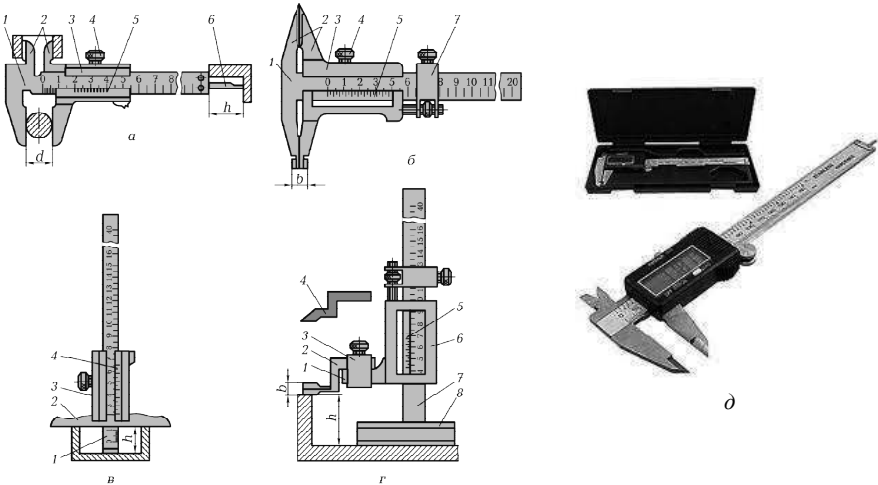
Штангенінструменти: а, б – штангенциркулі; 1 – штанга; 2 – губки для вимірювання зовнішніх і внутрішніх поверхонь; 3 – рамка; 4 – гвинт для фіксації рамки; 5 – ноніус; 6 – лінійка глибиноміру; 7 – пристрій точного переміщення рамки; в – штангенглибиномір: 1 – штанга; 2 – основа; 3 – рамка; 4 – ноніус; г – штангенрейсмус: 1 – виступ рамки; 2, 4 – вимірювальна ніжка; 3 – тримач вимірювальної ніжки; 5 – ноніус; 6 – рамка; 7 – штанга; 8 – основа; d – діаметр вимірюваної деталі; b – товщина вимірювальних губок; h – глибина отвору чи висота уступу; d – штангенциркуль із цифровою індикацією
